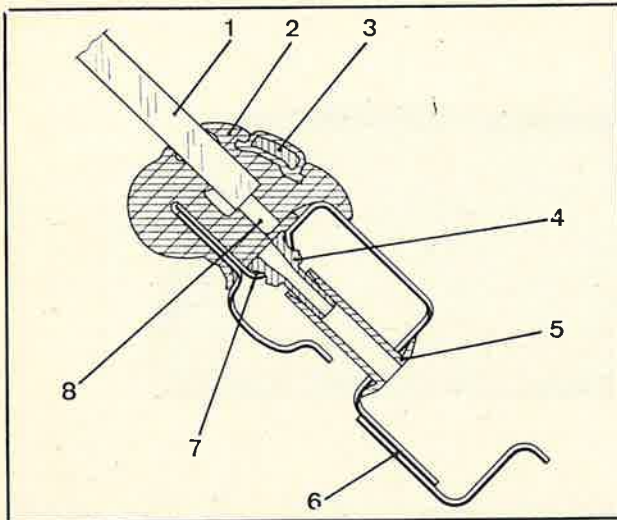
Vue en coupe de la lunette arrière et de son joint.
